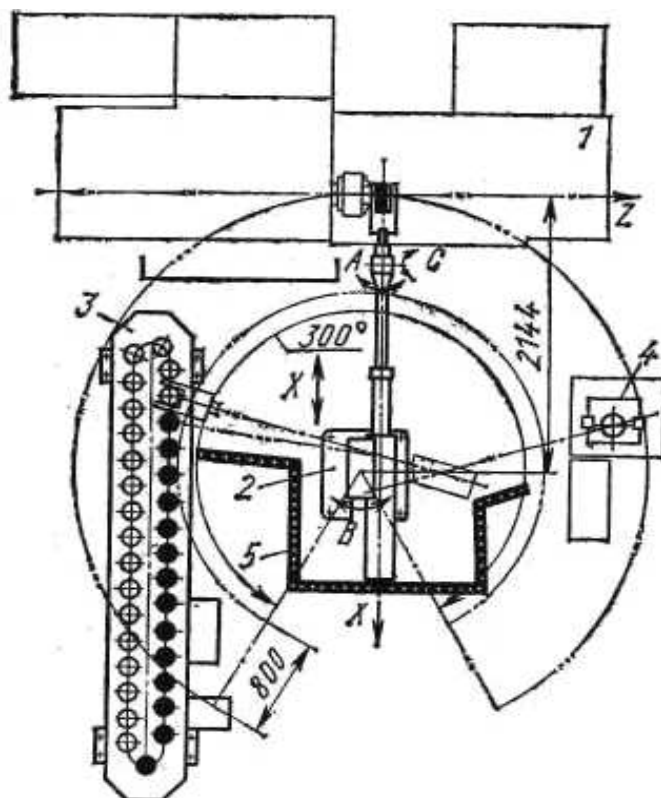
Гибкий производственный модуль для токарной обработки:
